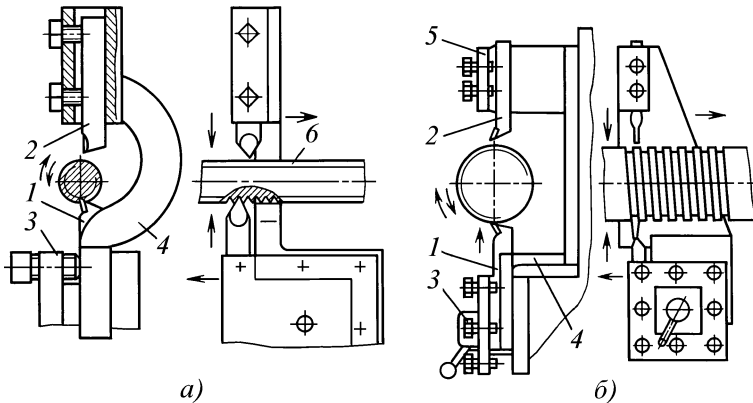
Схема нарезания резьбы с дополнительным резцедержателем:
